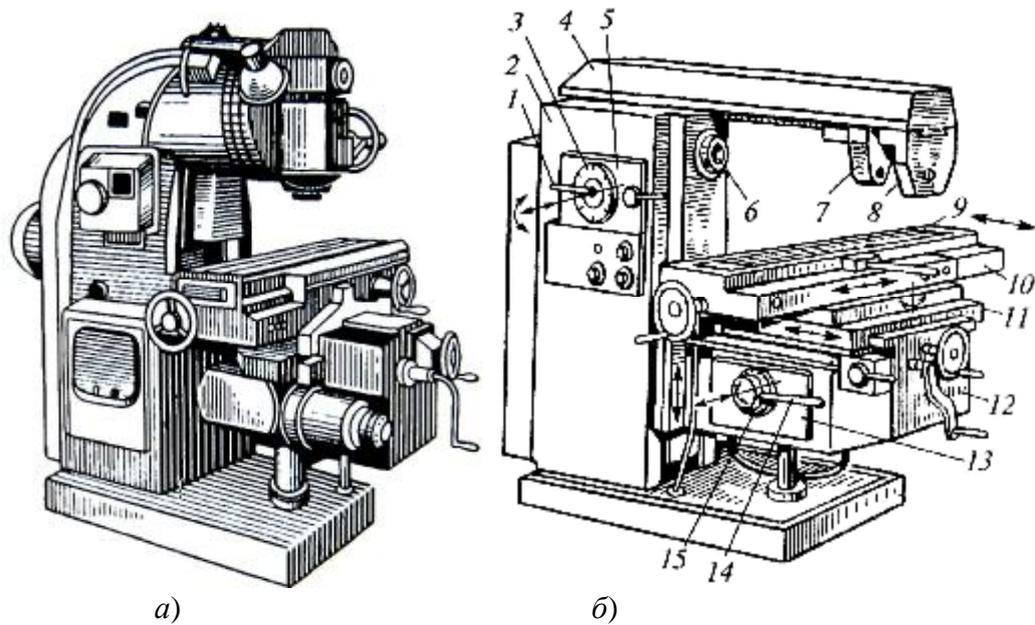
Вертикально-фрезерный (а) и горизонтально-фрезерный станки (б):
